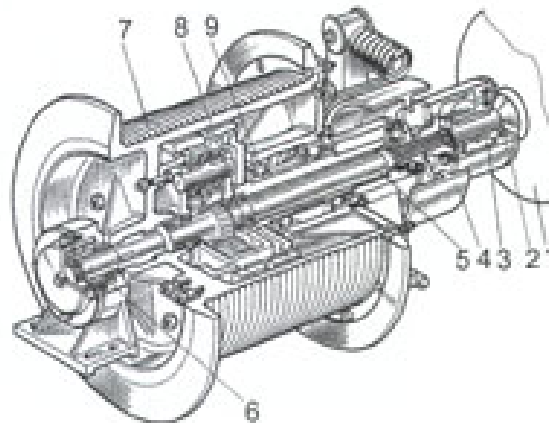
Конструкція вантажної лебідки з планетарним редуктором:
